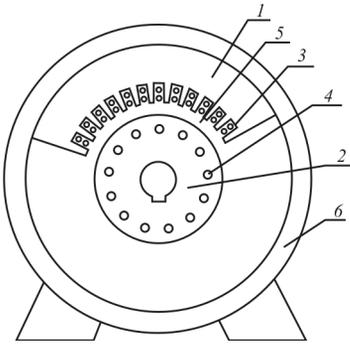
Асинхронный электродвигатель с дугообразной формой статора: 1 – стальной сердечник статора; 2 – стальной сердечник ротора; 3 – обмотка статора; 4 – обмотка ротора; 5 – воздушный зазор; 6 – корпус двигателя
